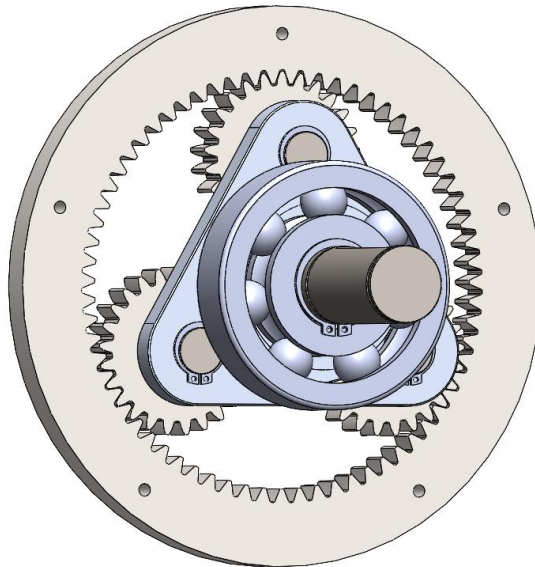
Ensamblaje CAD 3D de la caja de engranajes desde la perspectiva del eje de salida.
